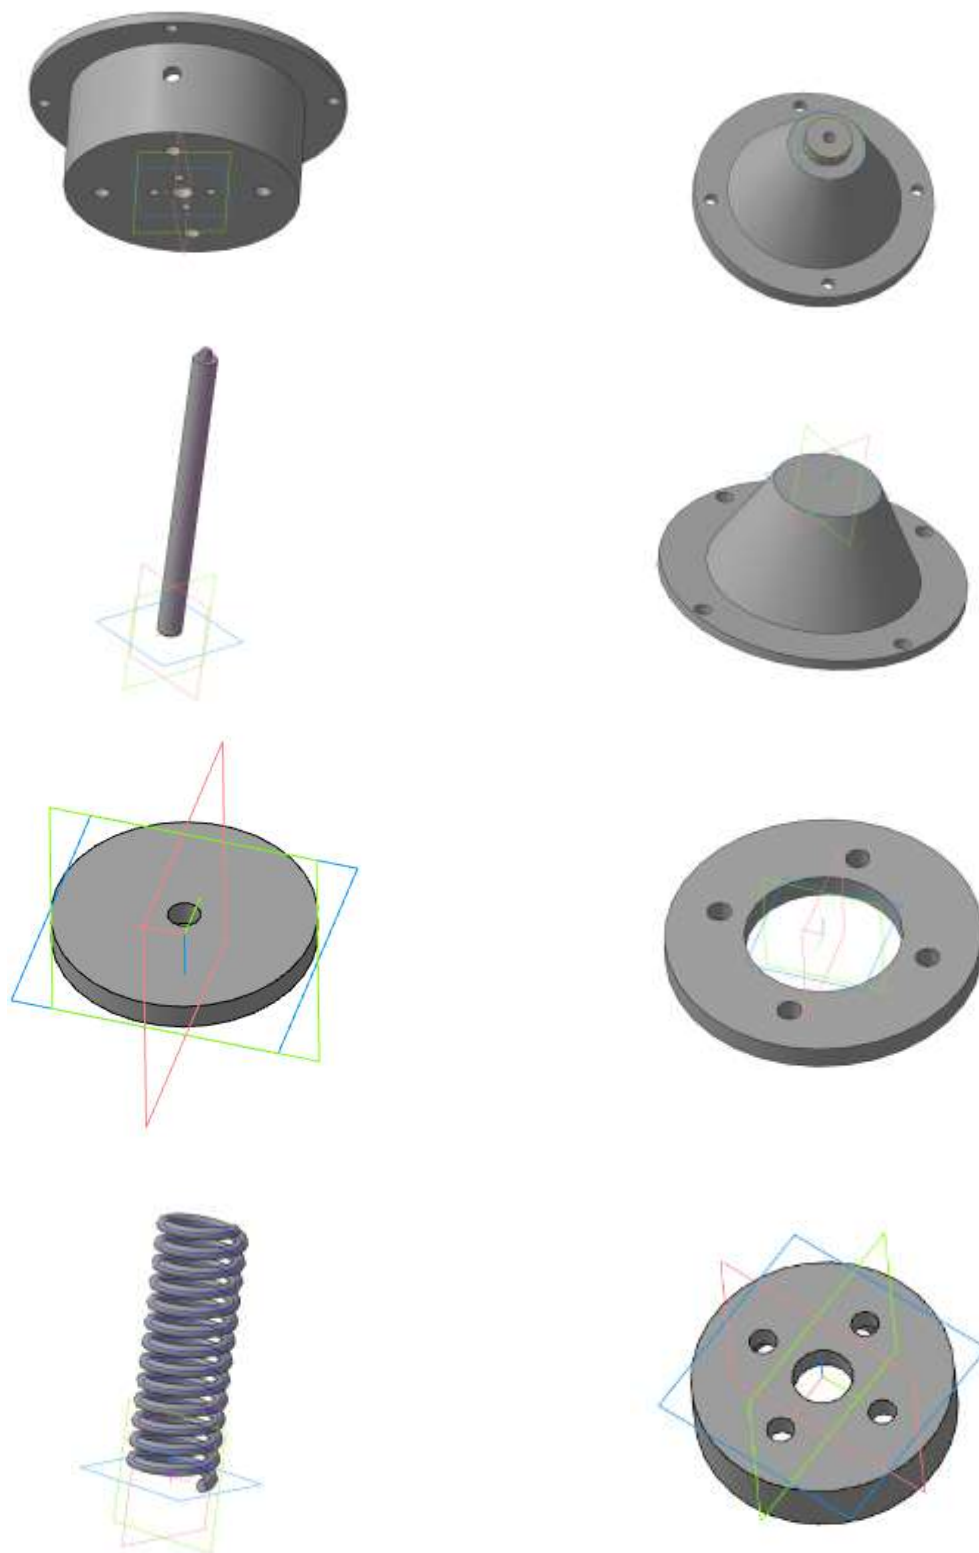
Камера Диафрагменная, детализовка 3D сборки
